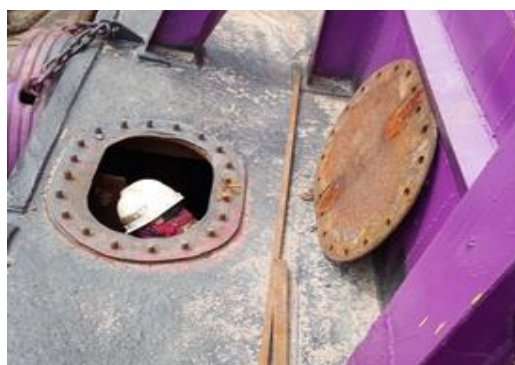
61 Welding Inspct Tangki Tongkang
